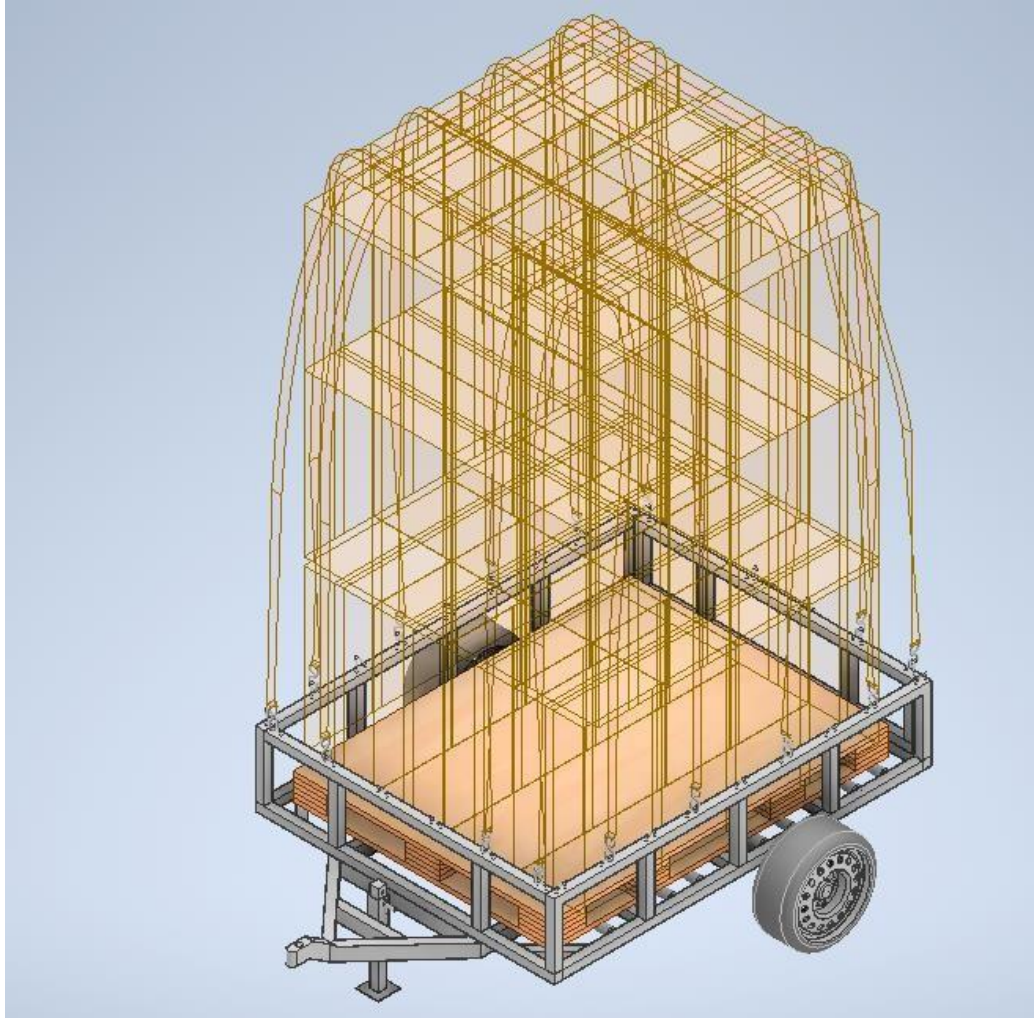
Diseño del remolque cargado del pallet. “Vista superior frontal derecha”
